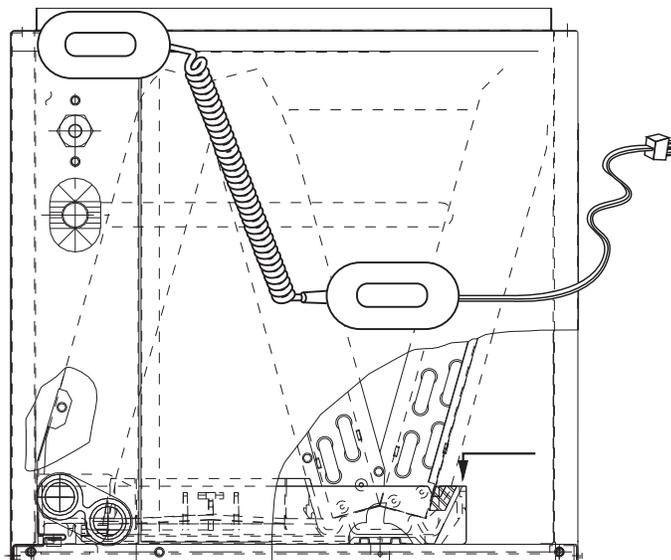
Assemblage de lampe UV (vue détaillée)
